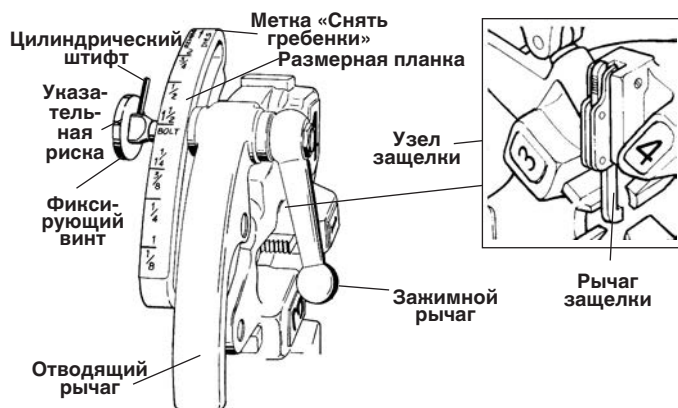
Универсальная самооткрывающаяся резьбонарезная головка
